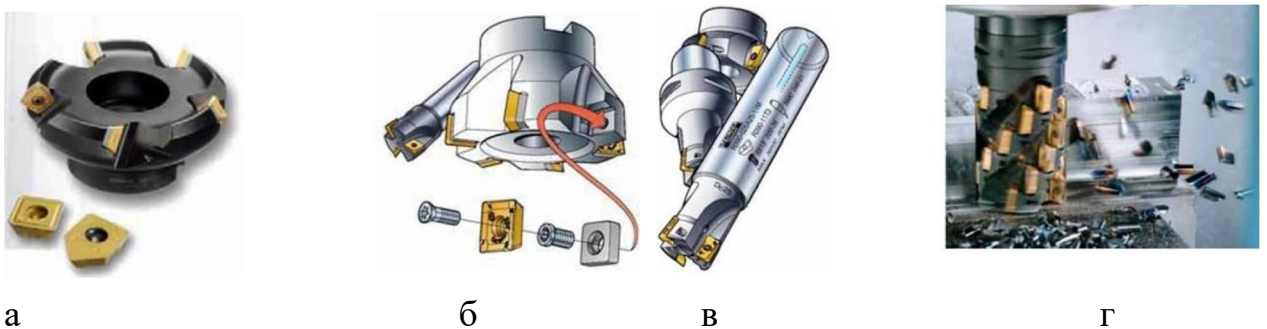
Фрези CoroMill 245 (а); CoroMill 290 (б); CoroMill 390 (в) і двокромочні (г)
